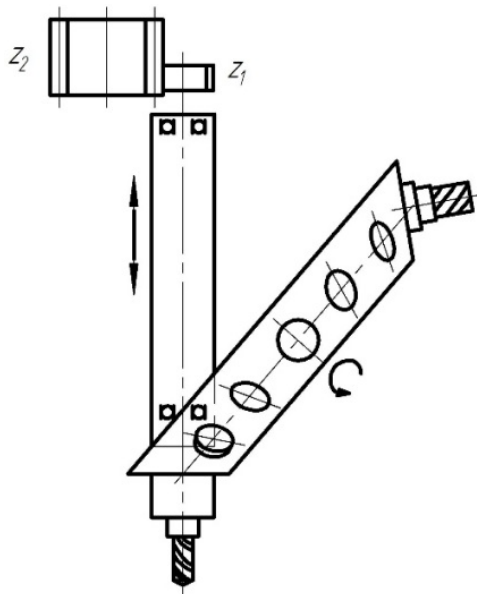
ПАЗІ з використанням револьверної головки для розширення набору інструментальних оправок
